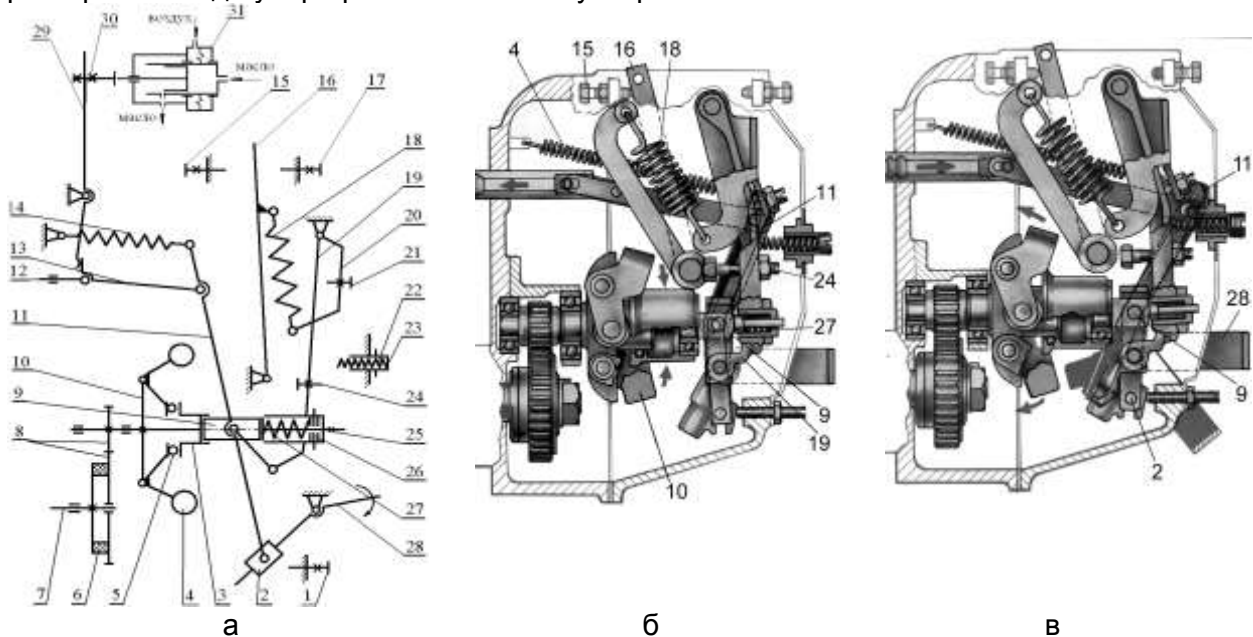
Схема регулятора ЯЗТА: 1 - винт кулисы; 2 - кулиса; 3 - муфта грузов; 4 - грузики; 5 - подшипник; 6 - демпфер; 7 - кулачковый вал; 8 - шестерни привода; 9 - упорная пятя; 10 - державка грузов; 11 - рычаг тяги; 12 - тяга рейки; 13 - рейка; 14 - пружина пускового обогатителя; 15, 17 - болты максимальной и минимальной частоты вращения; 16 - рычаг управления; 18 - пружина регулятора; 19 - рычаг регулятора; 20 - двуплечий рычаг; 21 - винт двуплечего рычага; 22 - буферная пружина; 23 - корпус буферной пружины; 24 - болт номинальной подачи; 25 - гайка хода штока корректора; 26 - регулировочная шайба натяжения пружины корректора; 27 - пружина корректора; 28 - скоба остановки двигателя; 29 - рычаг корректора; 30 - регулировочный винт; 31 - пневмогидрокорректор.
